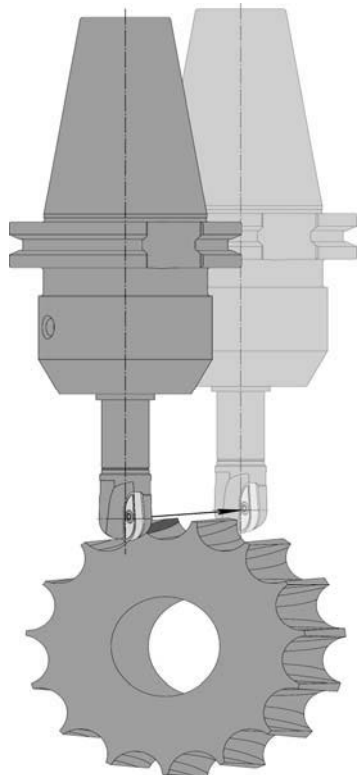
Схема формообразования участка поверхности зуба сателлита сферической фрезой на станке с ЧПУ
